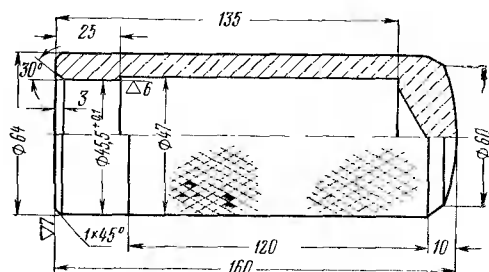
Оправка для запрессовывания сальника сектора рулевого механизма в картер
